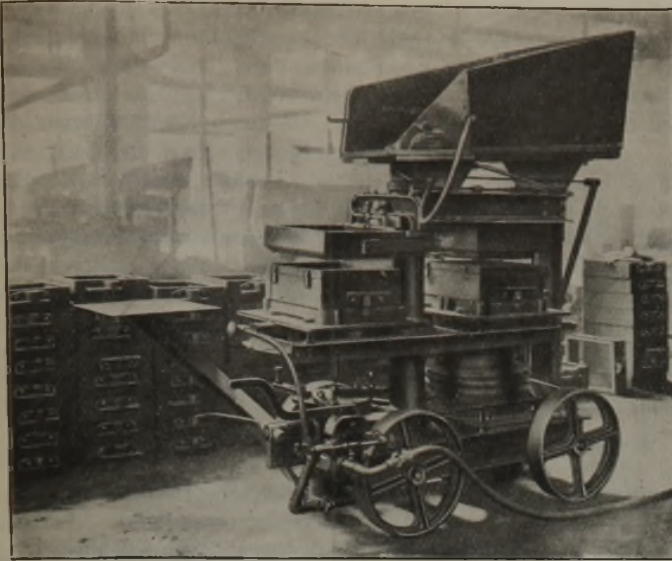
Fahrbare Drehtisch-Formmaschine.
